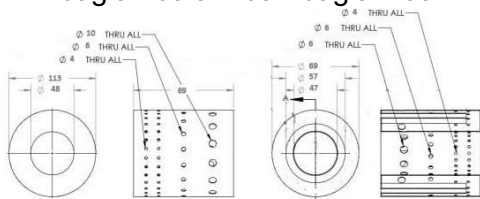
langkah pengerjaan untuk pembuatan *housing shaft*.
